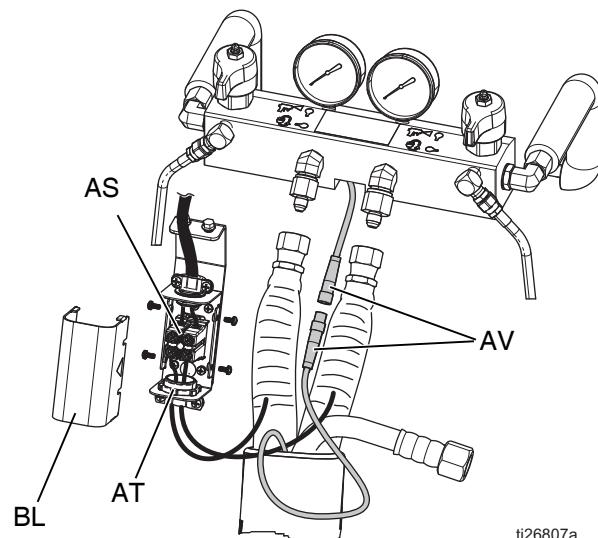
Boîtier de raccordement électrique du flexible chauffé
